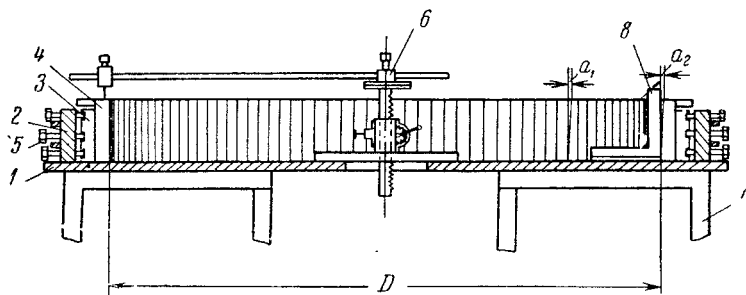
Кольцевое опрессовочное приспособление (еж) для сборки цилиндра меди
